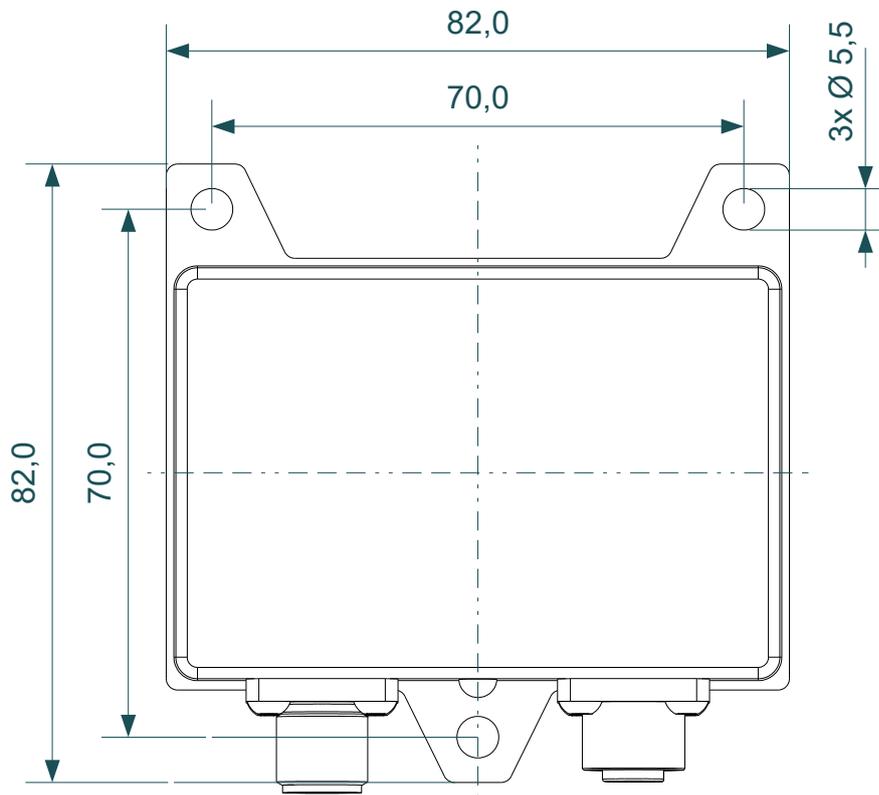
Befestigungsbohrungen Metallgehäuse (TK) (Maße in mm)
